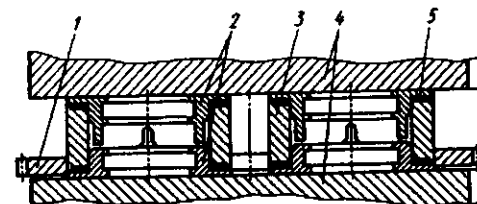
Кассета для доводки плоской поверхности детали типа фланца при двухрядном расположении деталей на двухдисковом станке с планетарным механизмом: 1 – кассета; 2 – детали; 3 – спутник; 4 – верхний и нижний притиры; 5 – прокладка
